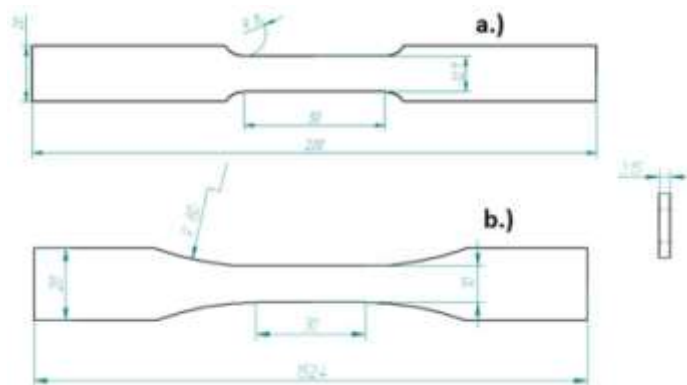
Dimensiones en mm de las probetas utilizadas en a) prueba a tensión y b) prueba de fatiga
